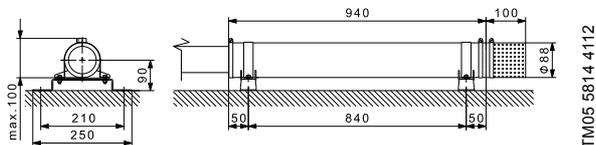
Kühlmantel und Einlaufsieb für die 3"-SQFlex
